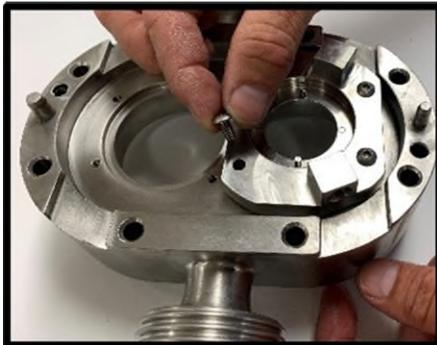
Herausnehmen der Schrauben des Dichtungsgehäuses
